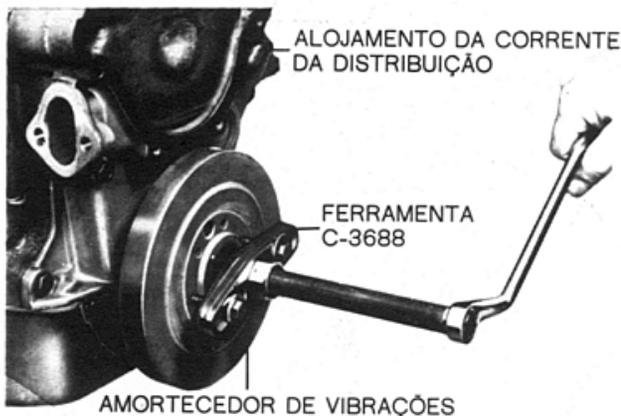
Remoção do conjunto do amortecedor de vibrações
